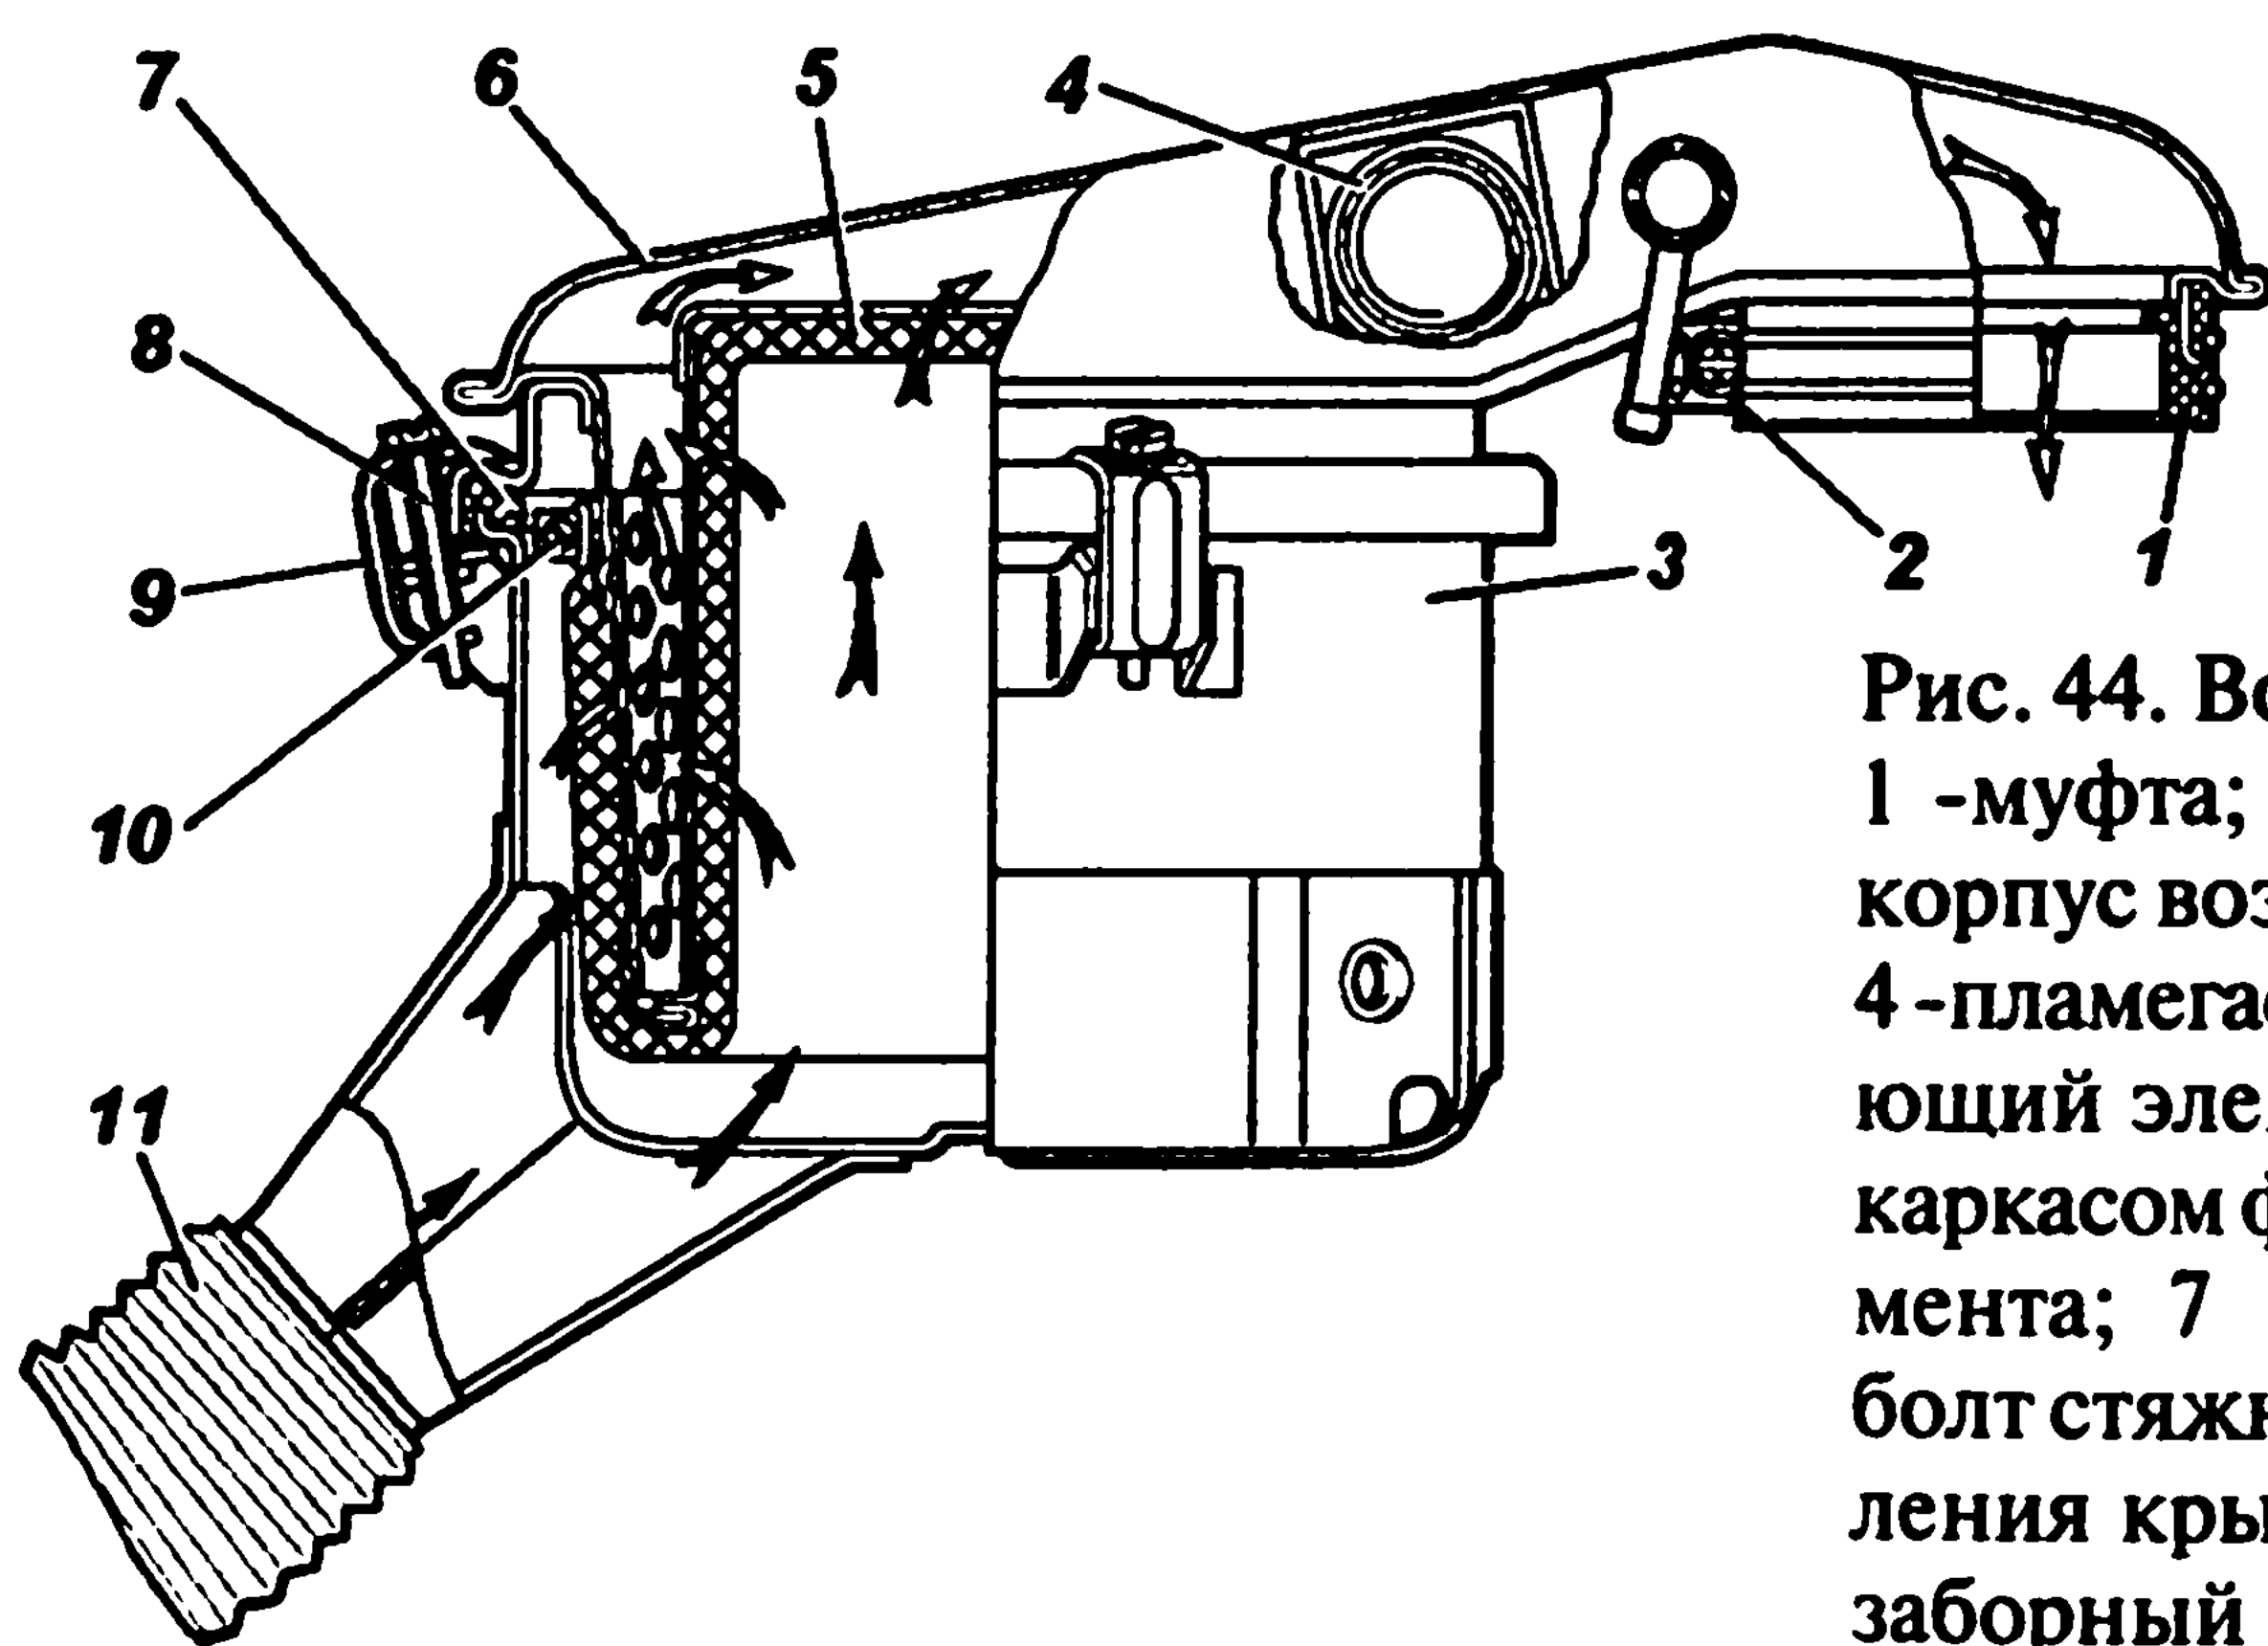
Воздушный фильтр: 1 - муфта; 2, 10 - хомуты; 3 - корпус воздушного фильтра; 4 - пламегаситель; 5 - фильтрующий элемент; 6 - крышка с каркасом фильтрующего элемента; 7 - уплотнитель; 8 - болт стяжной; 9 - скоба крепления крышки; 11 - воздухозаборный рукав
